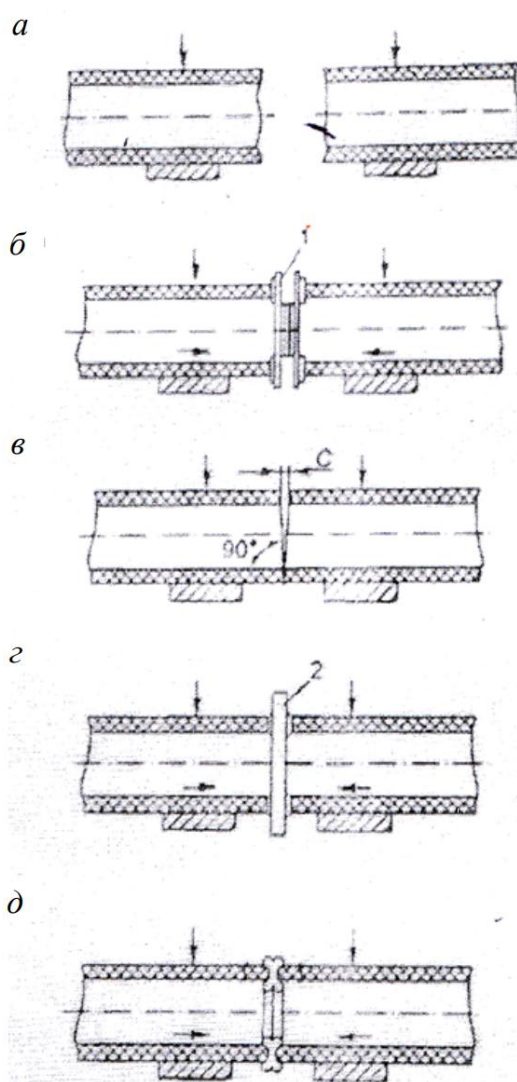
Последовательность процесса сборки и сварки встык труб из полиэтилена:
